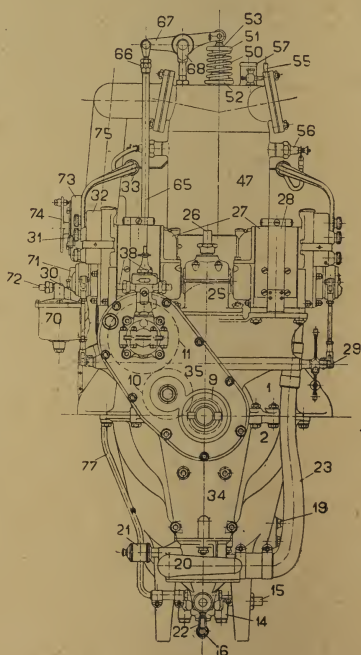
Sechszylinder-Argus-Flugmotor. Stirnseite.
